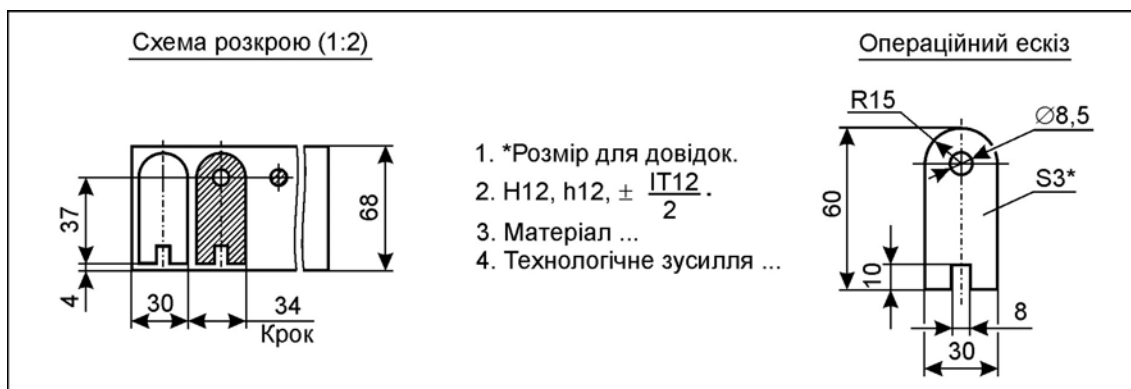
Приклад оформлення операційного ескізу та схеми розкрою штампа для виготовлення деталі «Упор» (штамп послідовної дії для пробивання та вирубання)
